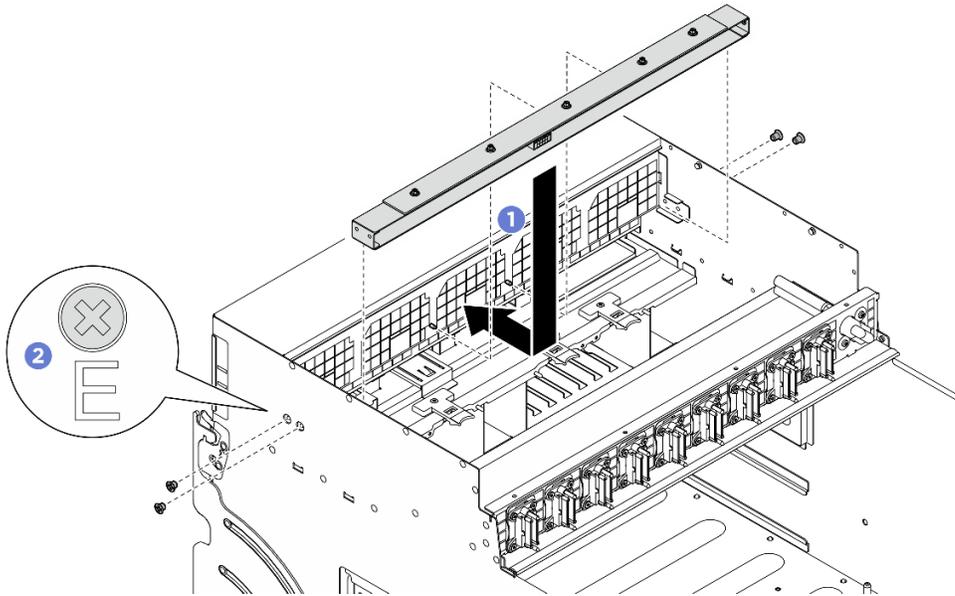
Instalación del conjunto placa de control del ventilador frontal
